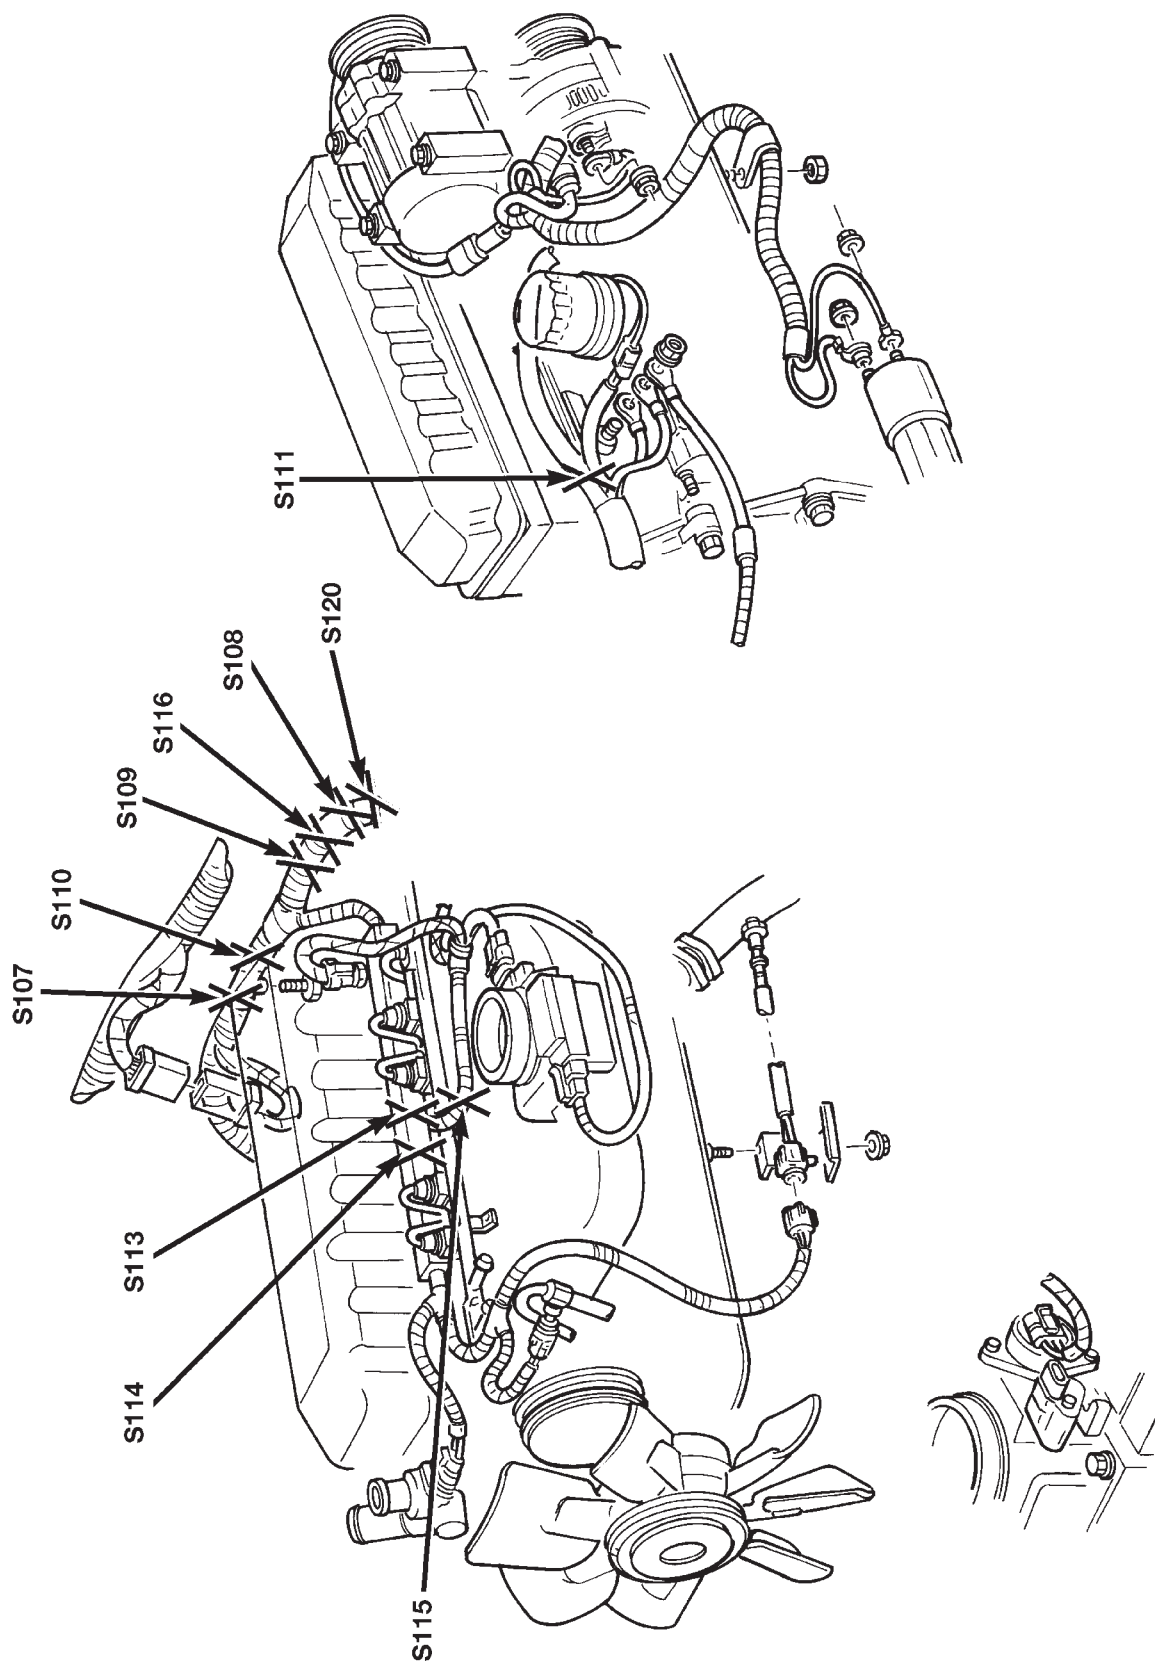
Empalmes de cableado del motor - Motor 2.5L LHD
